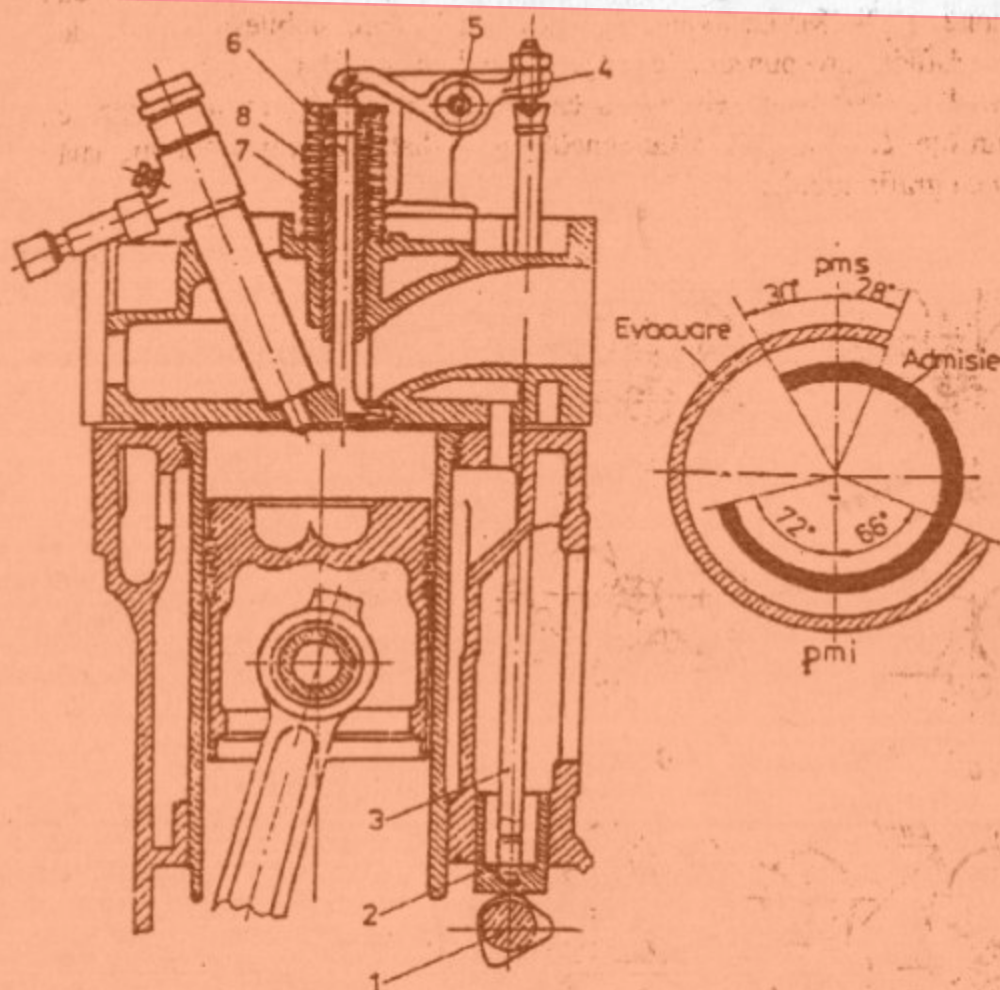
Mecanismul de distribuție a gazelor pentru motorul D-110:
